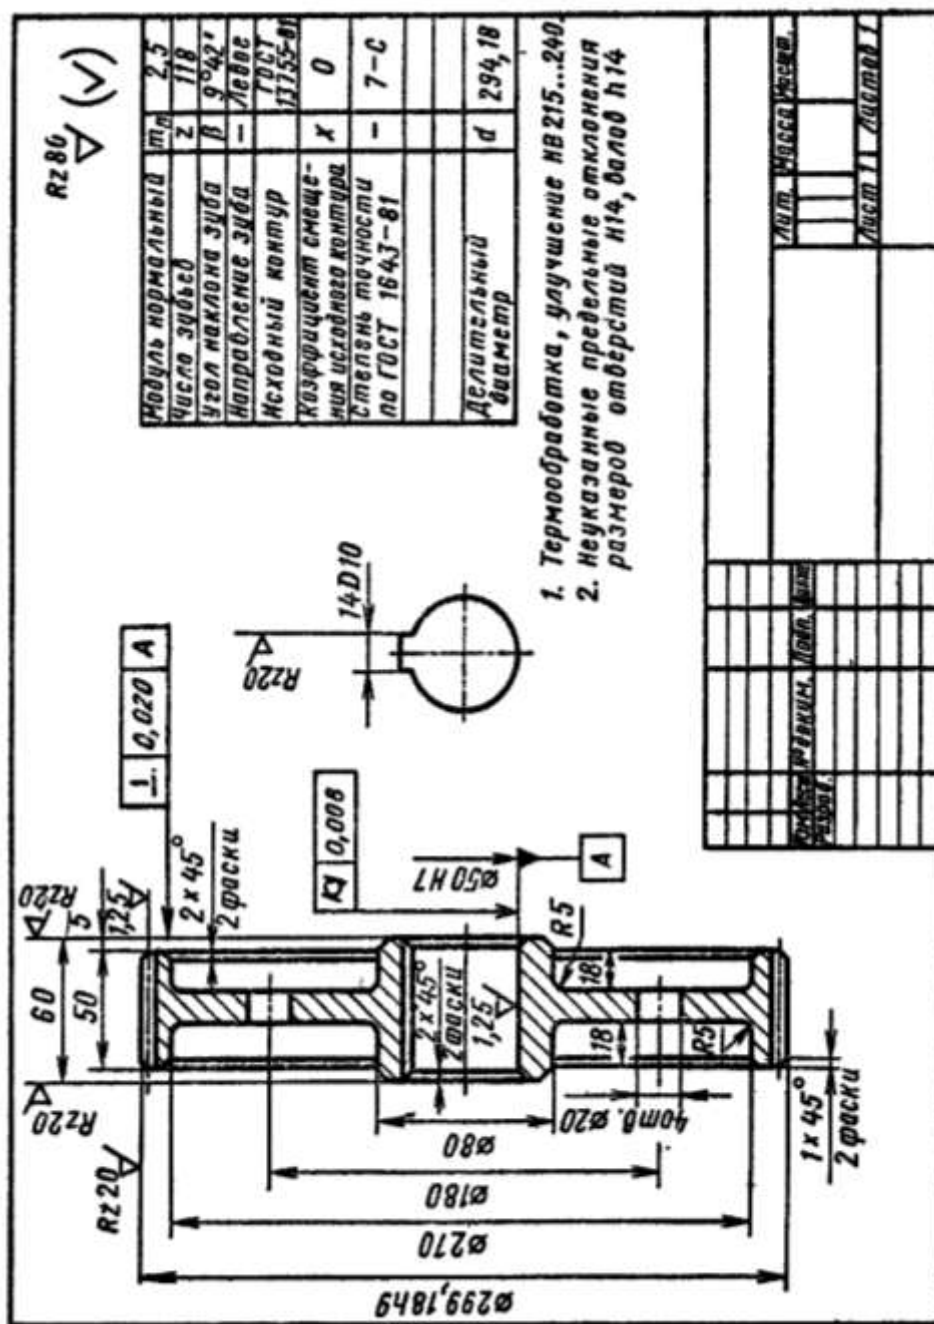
Пример выполнения рабочего чертежа зубчатого колеса.
